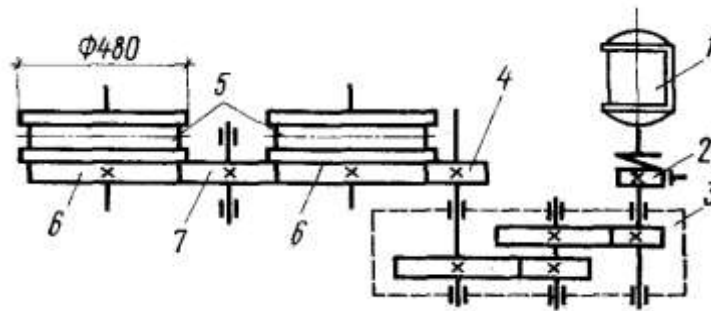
Кінематична схема ходового пристрою з жорсткими металевими колесами:
